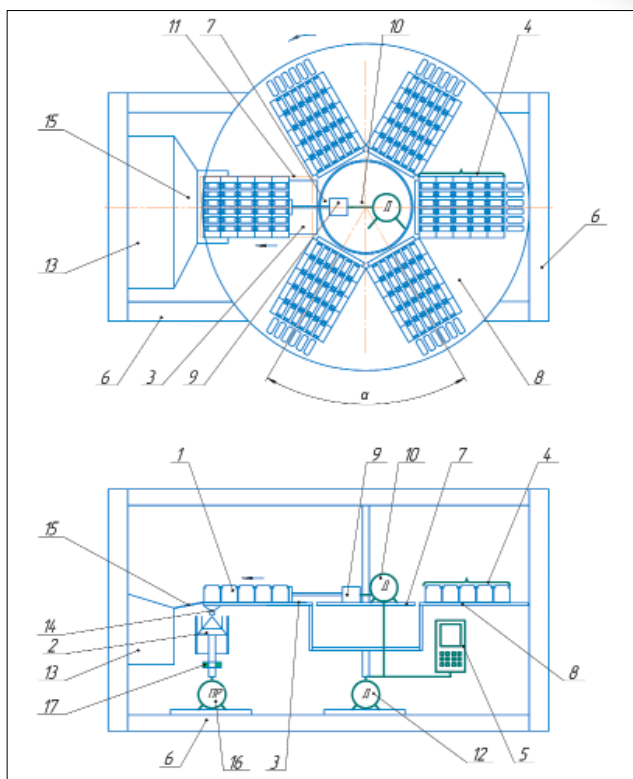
Схема РКЗУ карусельного типа (вид сверху и сбоку): 1 – кассета с ячейками для высеваемого материала; 2 – высевающий аппарат; 3 – направляющая пластина; 4 – кассетный блок; 5 – блок управления; 6 – рама; 7 – центральная неподвижная платформа; 8 – внешняя подвижная платформа; 9 – актуатор; 10 – электродвигатель привода актуатора; 11 – рабочая зона перемещения кассет; 12 – шаговый электродвигатель привода внешней подвижной платформы; 13 – контейнер для сбора пустых кассет; 14 – рабочий стол с отверстиями для выгрузки семян из ячеек кассеты; 15 – наклонный лоток для спуска пустых кассет; 16 – шаговый электродвигатель привода высевающего аппарата; 17 – датчик вращения конусных высевающих аппаратов
